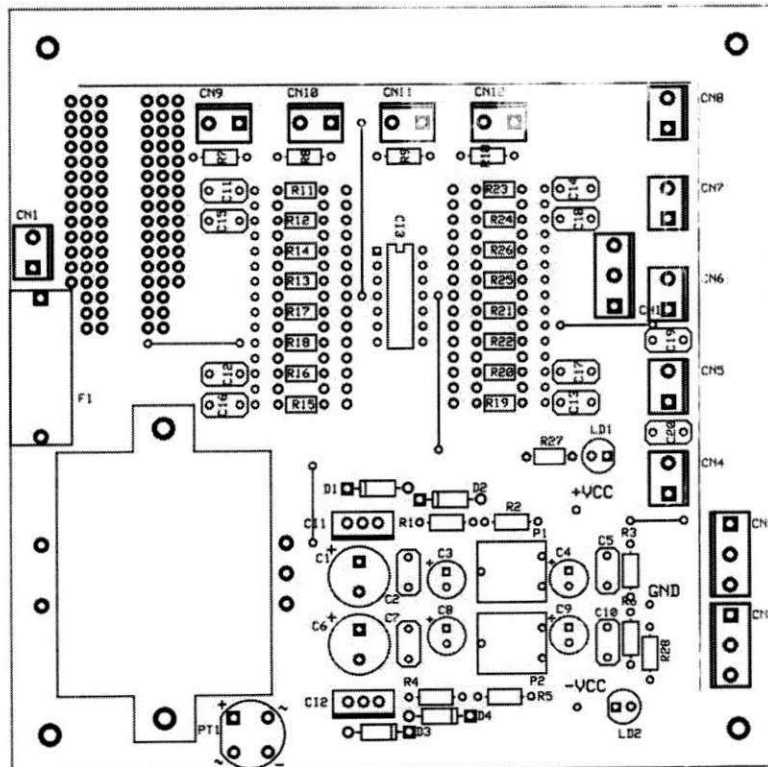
Layout da placa de circuito impresso (serigrafia e lado componentes).
